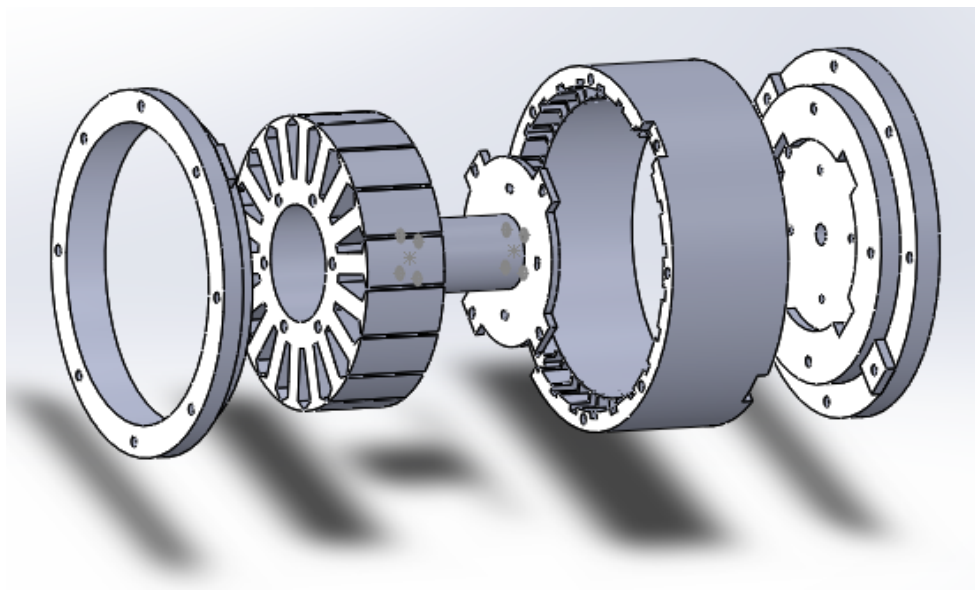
Sestava čela rotoru s čepem pro uložení do ložisek statoru
